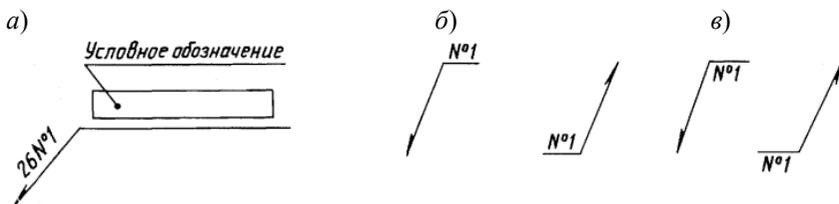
Условное обозначение одинаковых сварных швов
